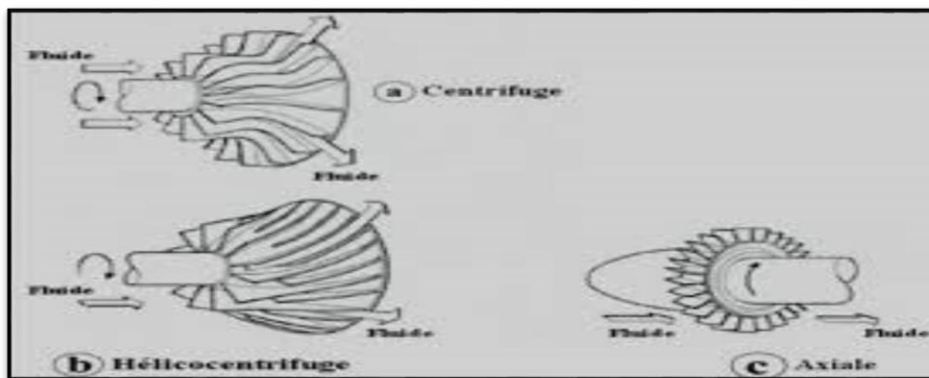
Roues mobiles de machines centrifuge, hélico centrifuge et axiale. [13]
